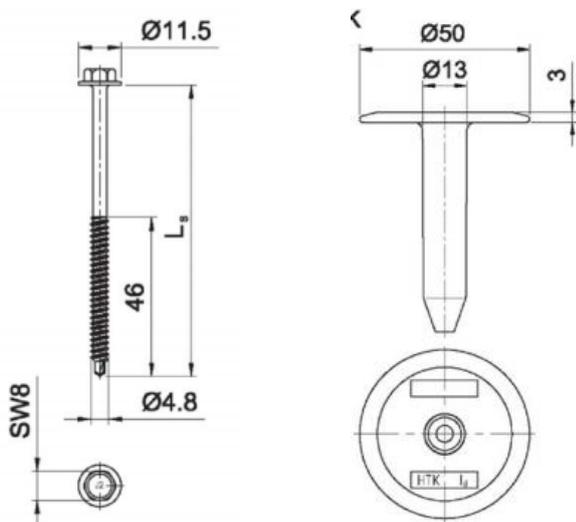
Vue EJOT DABO TKR-4,8 + tube HTK
